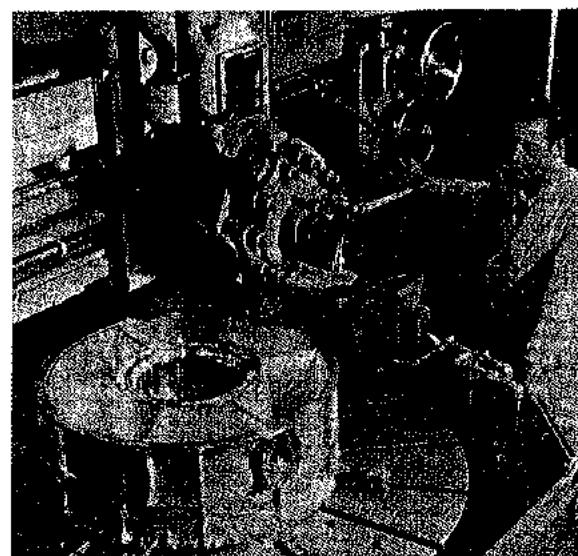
Mecanizado en el torno revólver vertical de una pieza fundida de compresor de admisión para motor de reacción (Bullard Co.).
